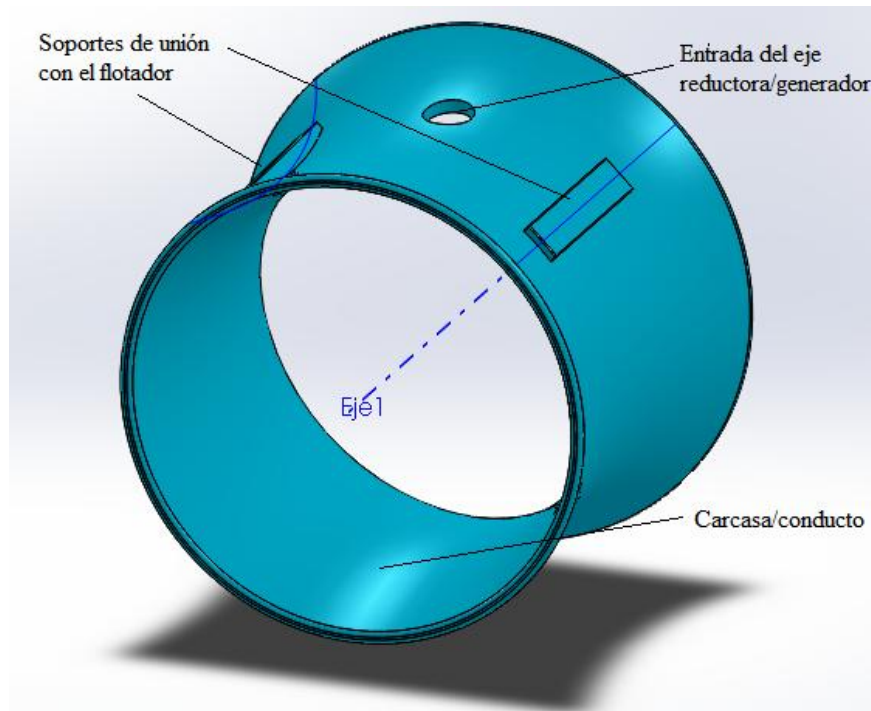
5. Diseño de la carcasa/conducto Fuente: diseño propio.
